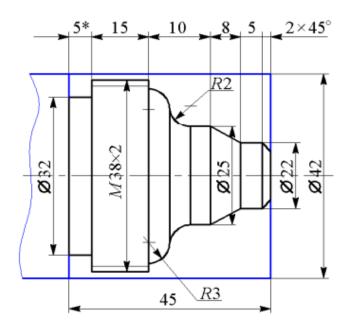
Эскиз обрабатываемой детали для подгруппы 1
